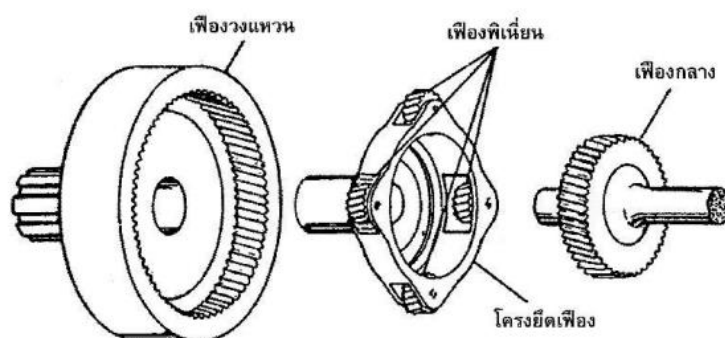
ชุดเฟืองแพลนเนตารี (Planetary Gear) [8]
